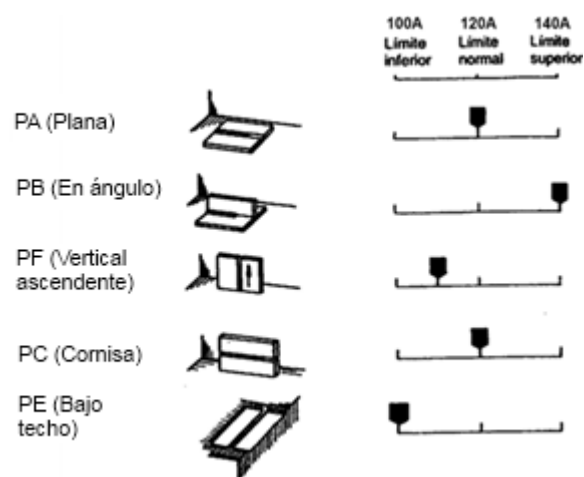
Intensidad de la soldadura en función de la posición. Chapa de 3mm d espesor, soldada en una pasada.
